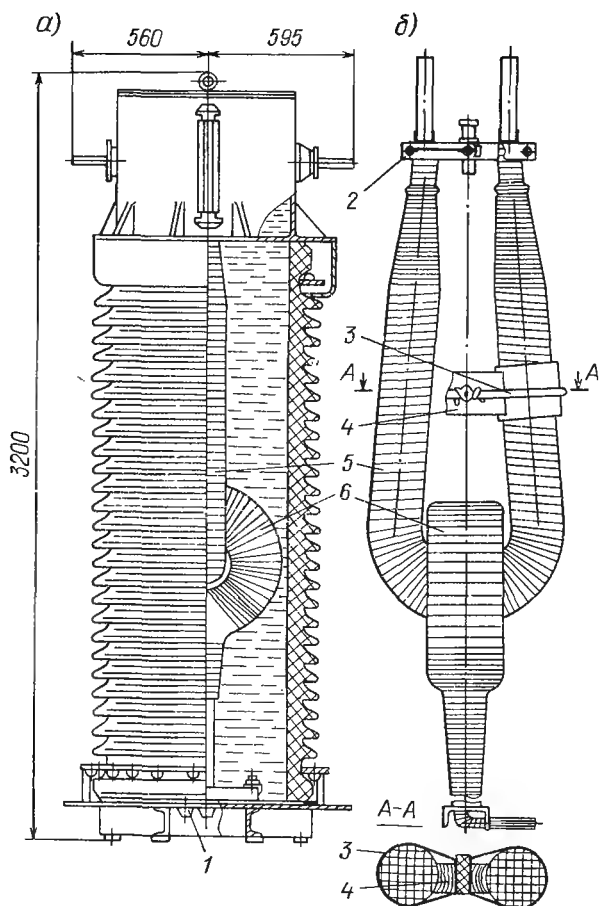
Трансформатор тока ТФЗМ500Б-У1, верхняя ступень: а — разрез; б — обмотки
